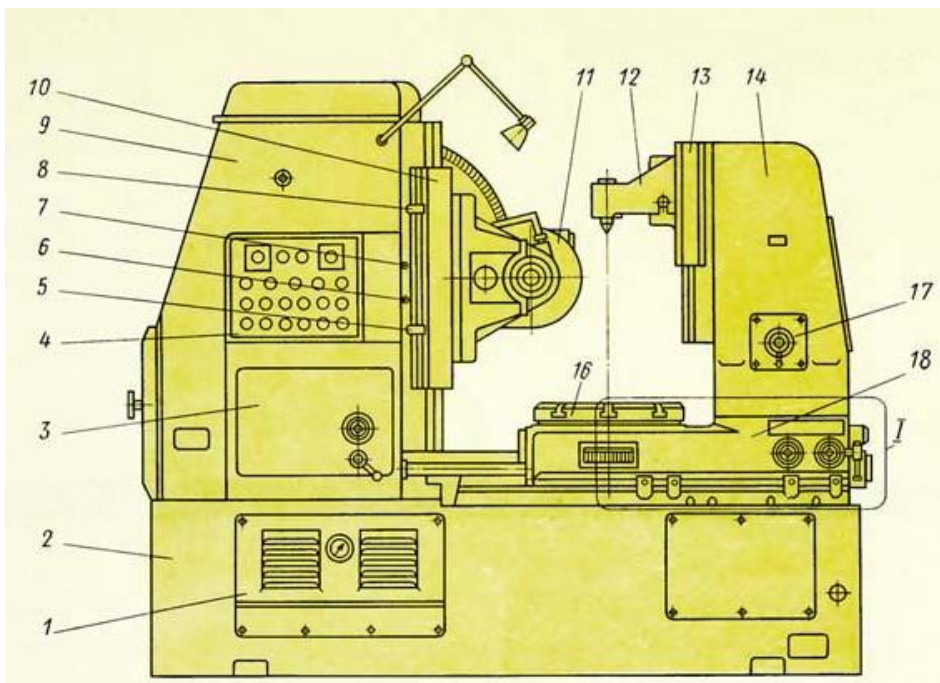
Загальний вид зубофрезерного верстата моделі 5К324А
